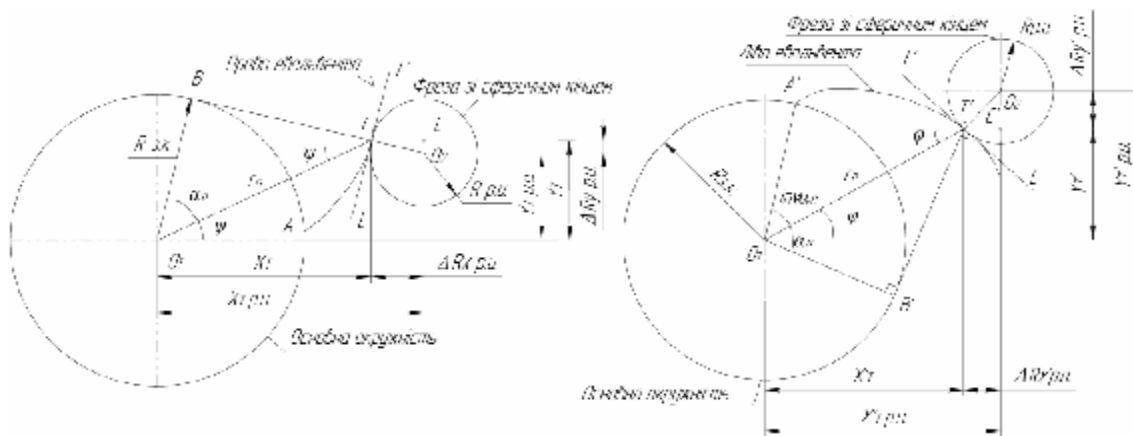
Розташування фрези на лівій та правій евольвентній поверхні у процесі обробки (вид з гори)
